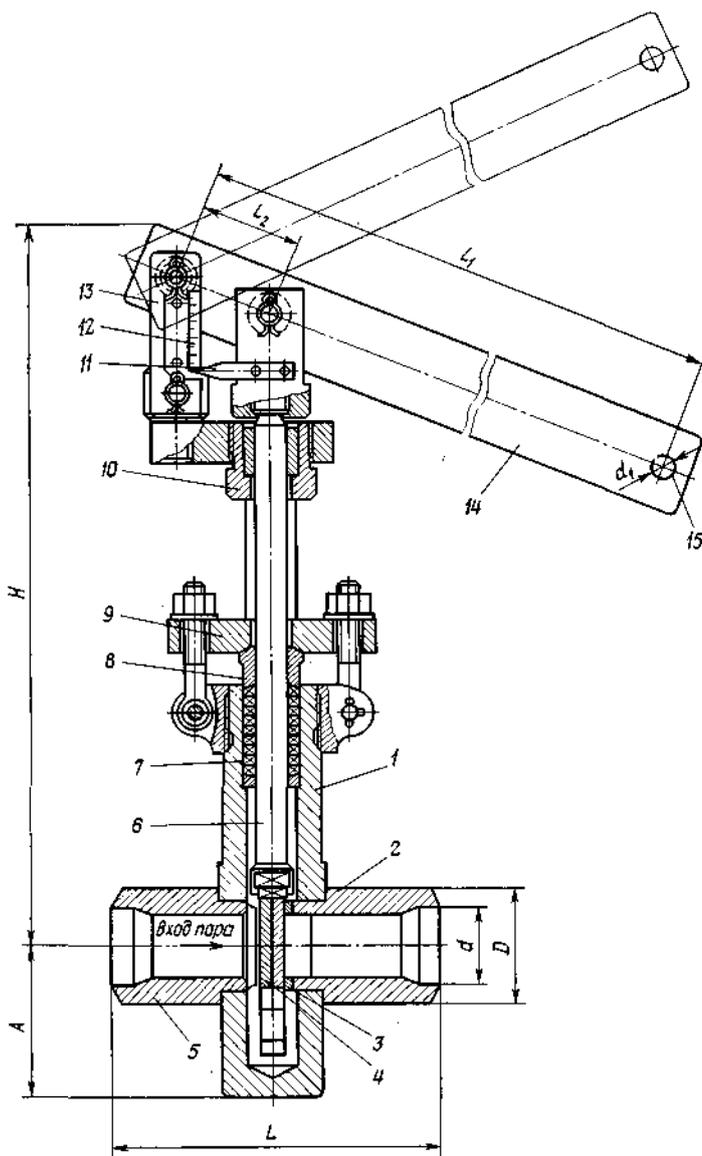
Клапан дроссельный шиберного типа Ду 40, 50, 65 серий 815, 811, 808
